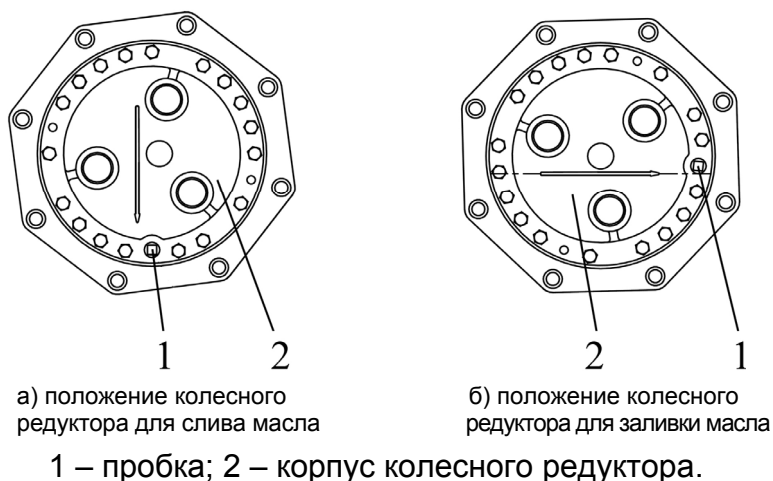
Замена масла в корпусах колесных редукторов
